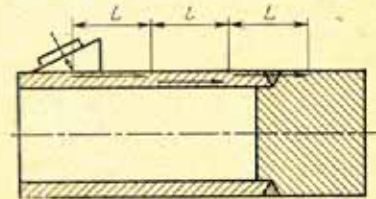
Контроль сварного шва трубы и втулки псевдорелевской волной
